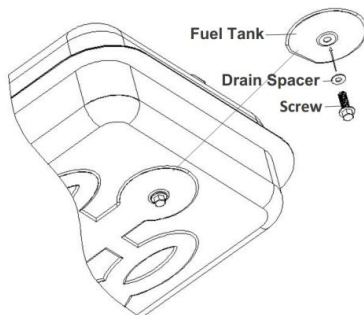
Ablassschraube entfernen. Pumpendruck einstellen
